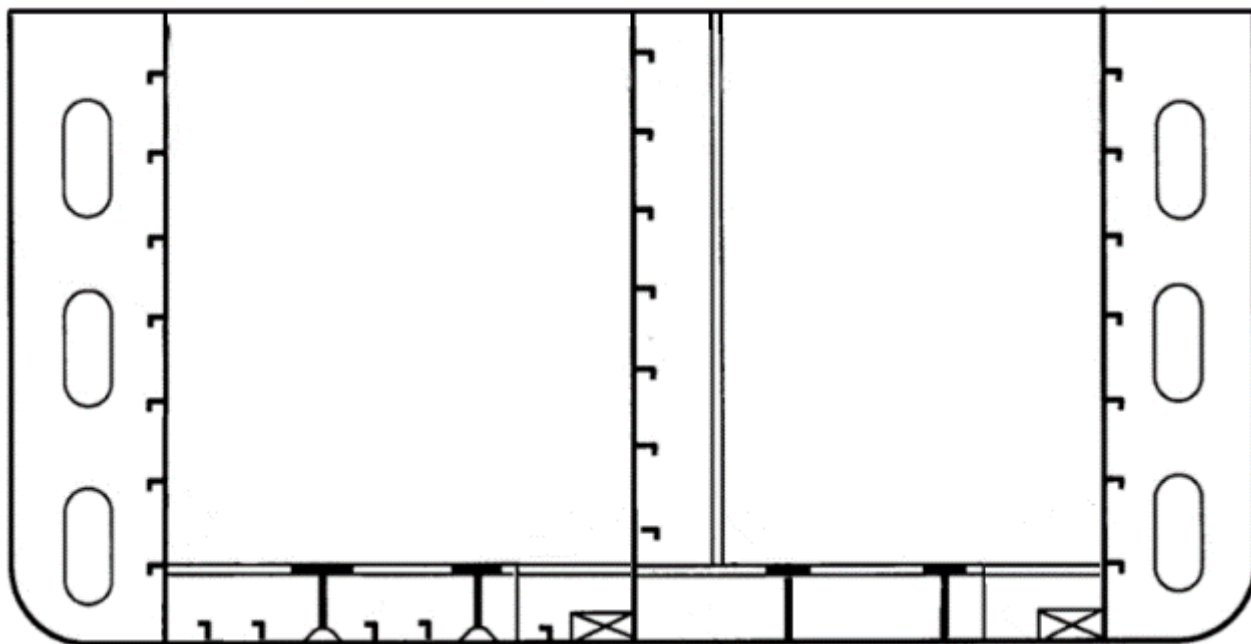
Эскиз общего вида резервуаров РП-1300
